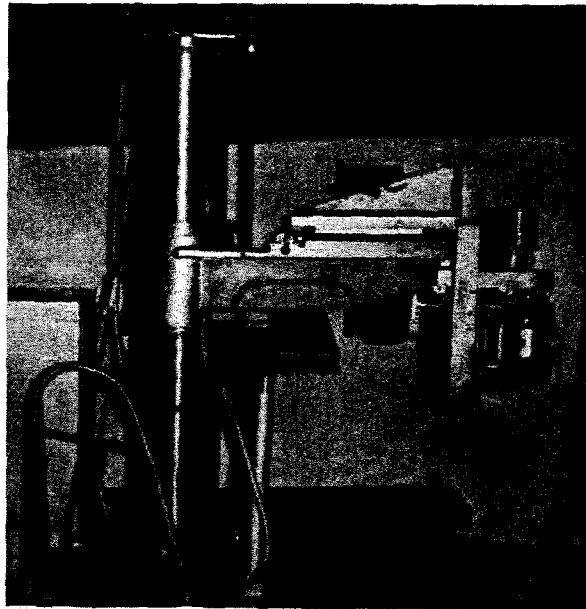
Общий вид опытно-промышленного образца установки модели СФТ2.126 для магнитно-абразивной зачистки кромок деталей
